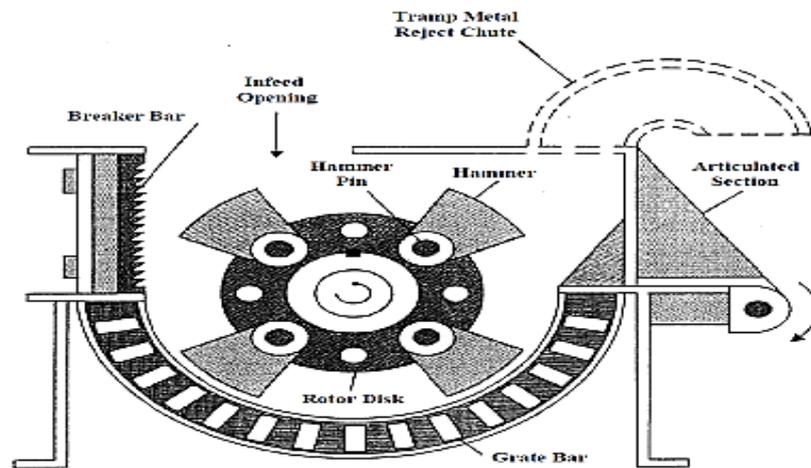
Coupe d'un hammermil horizontal. [32]
